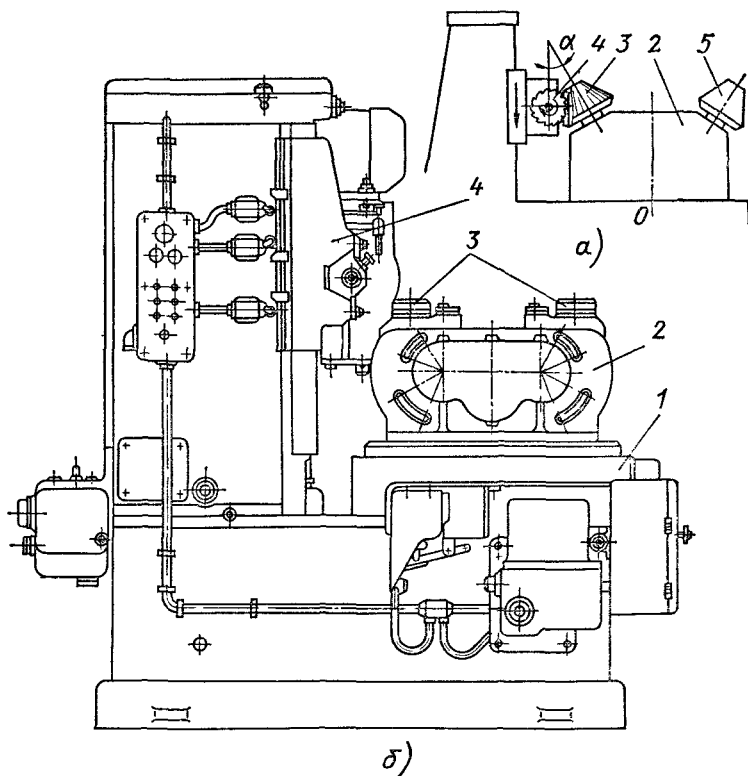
Зубофрезерный станок мод. ЕЗ-40
